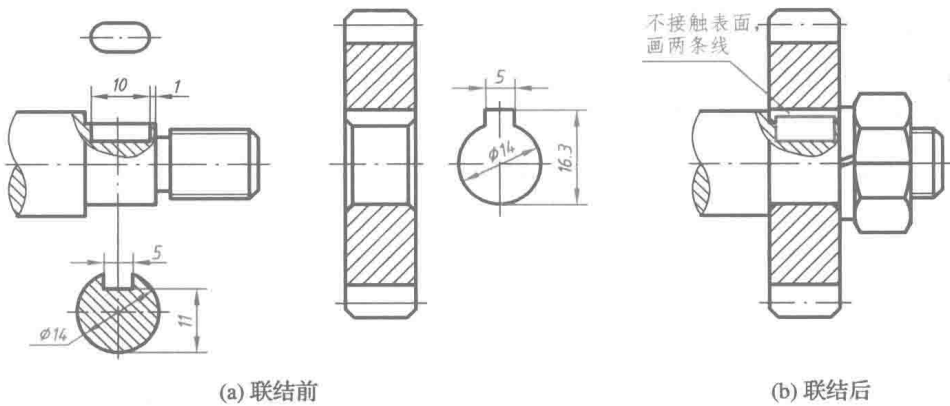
轴和轮毂上的键槽的画法和尺寸注法以及它们用键联结后的装配画法
